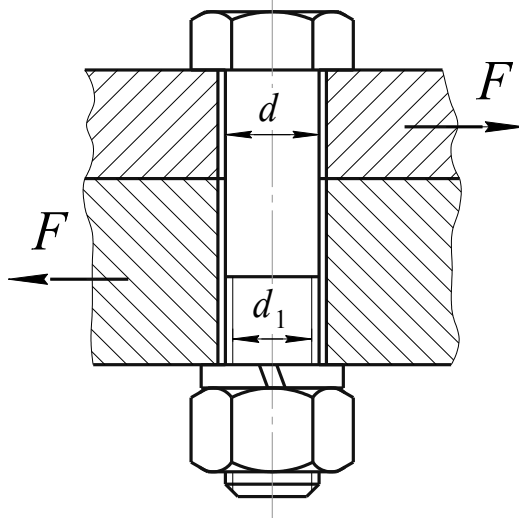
Схема расчёта резьбового соединения (случай 4)
